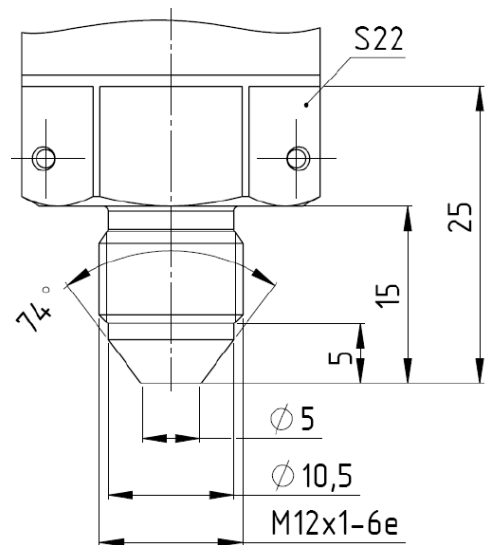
Присоединительный штуцер тип 4 по ГОСТ 19125-90, исп. 1, черт. 2
